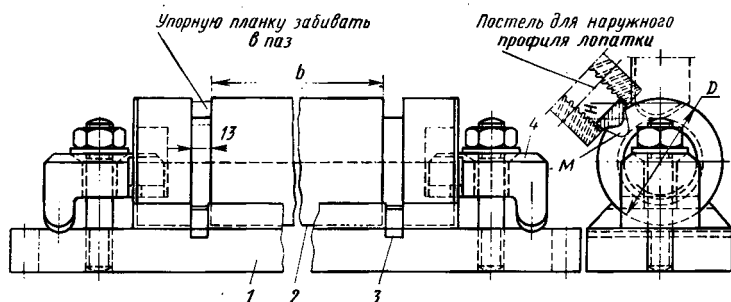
Универсальное приспособление для обработки внутренних профилей лопаток постоянного сечения длиной до 450 мм
